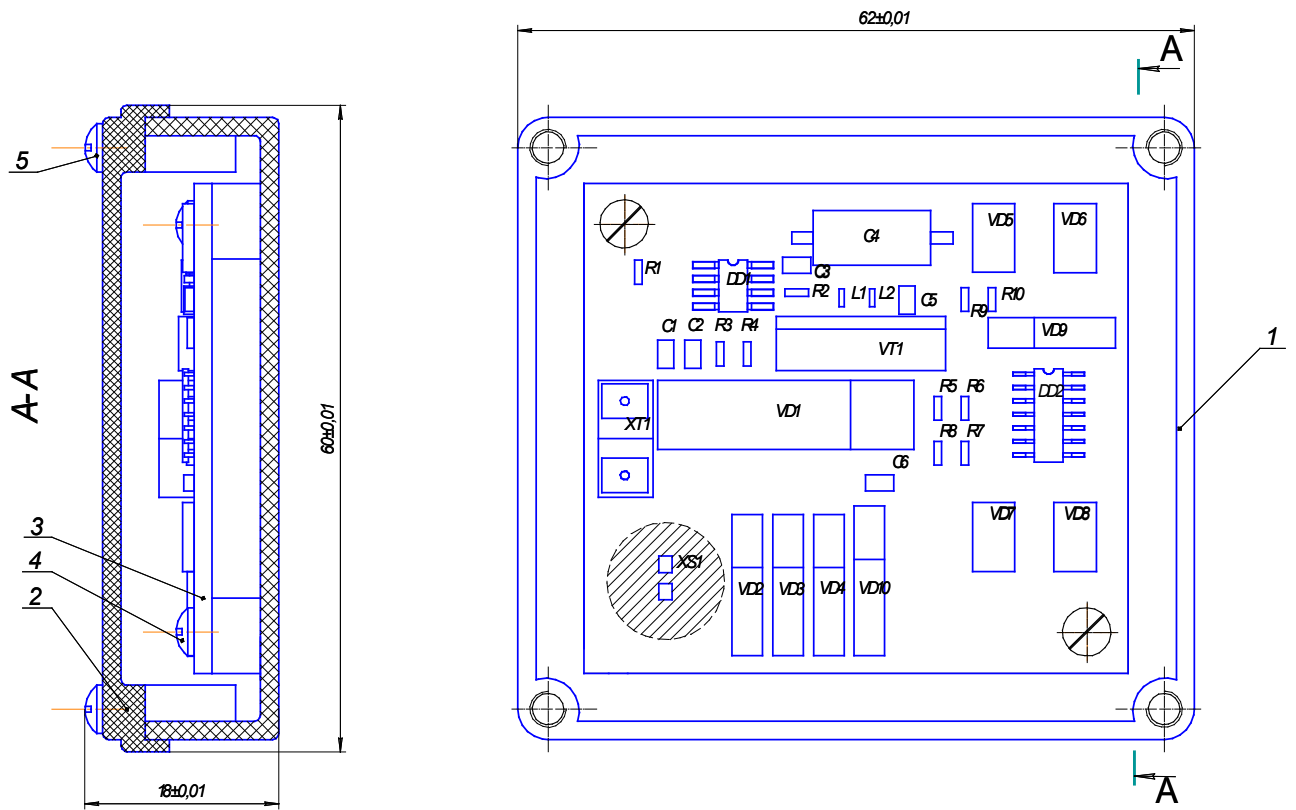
Пример платы печатной в сборе (с корпусом и крышкой)
